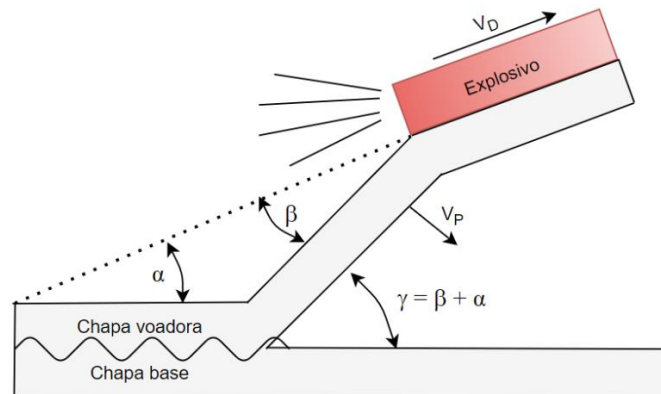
Configuração oblíqua do processo de soldadura por explosão. Adaptado de [48].
